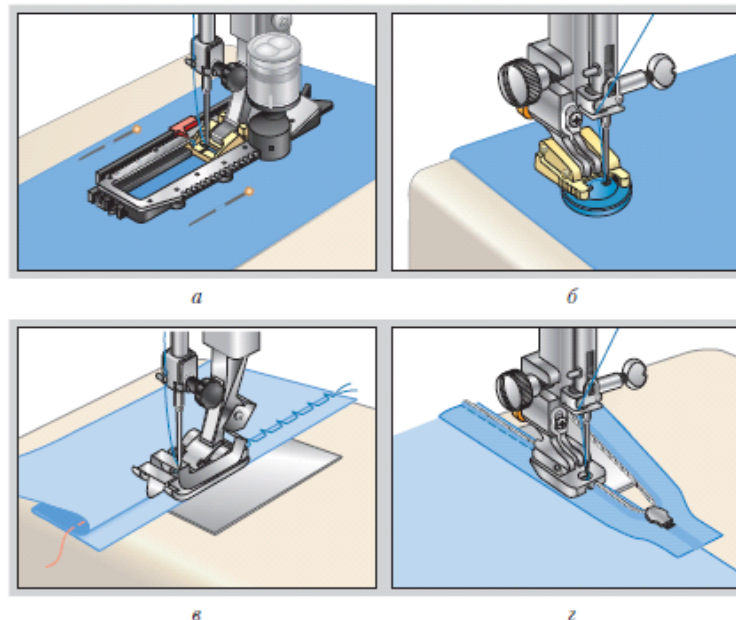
Приспособления к швейной машине: а – лапка для обметывания петель; б – лапка для пришивания пуговиц; в – лапка для потайного подшивания; з – лапка для притачивания потайной застёжки-молнии
